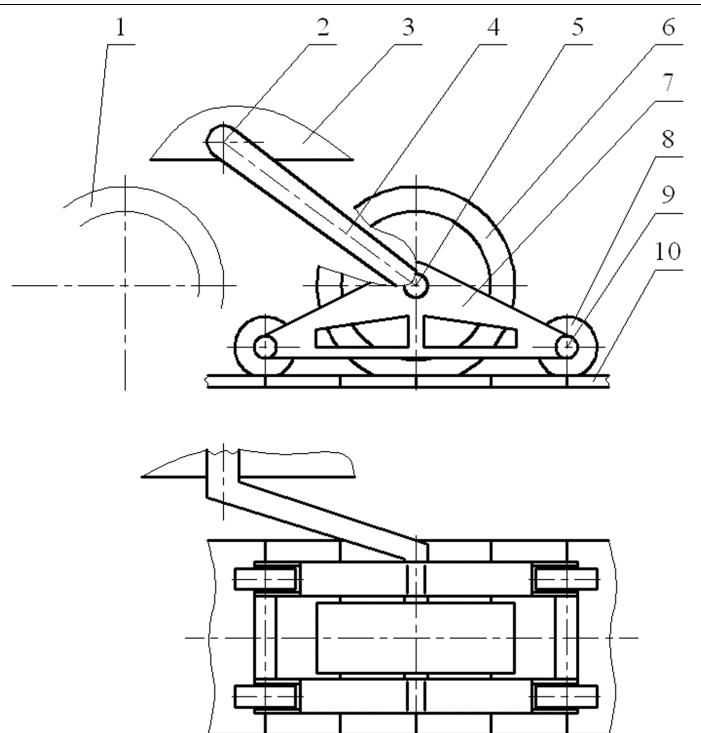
Успокоитель гусеницы: 1 – смежный опорный каток; 2 – ось заделки (верхней головки) балансира; 3 – корпус машины; 4 – тело балансира; 5 – ось опорного катка; 6 – опорный каток с массивной шиной; 7 – тележка (рама); 8 – дополнительный опорный каток; 9 – ось дополнительного опорного катка; 10 – участок опорной ветви звенчатой гусеницы
